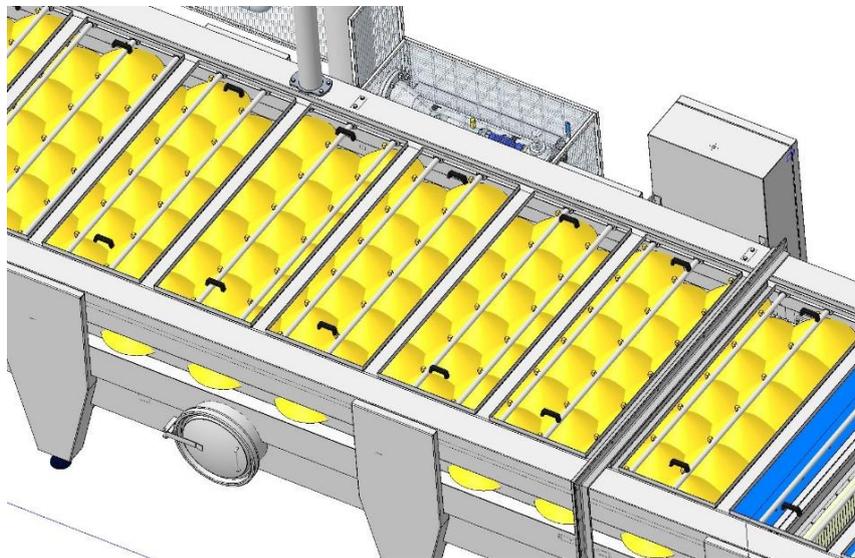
Tunnel di trattamento termico, vista interna lato ugelli
